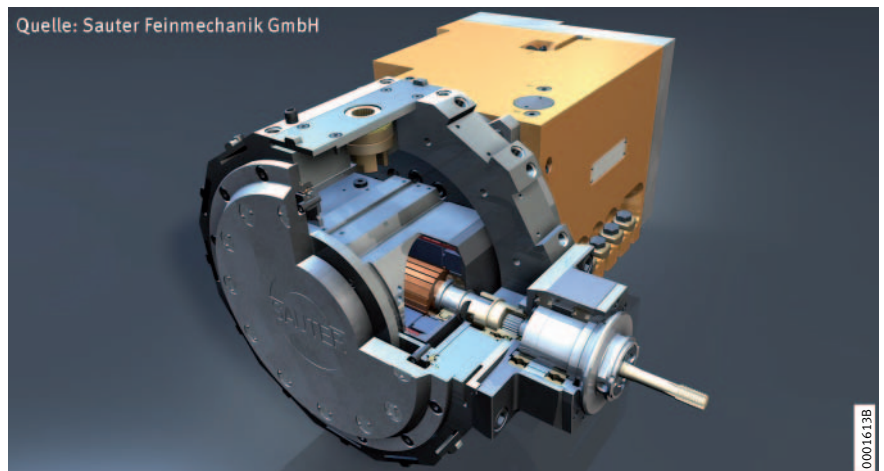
Angetriebenes Werkzeug (Schnittbild)
